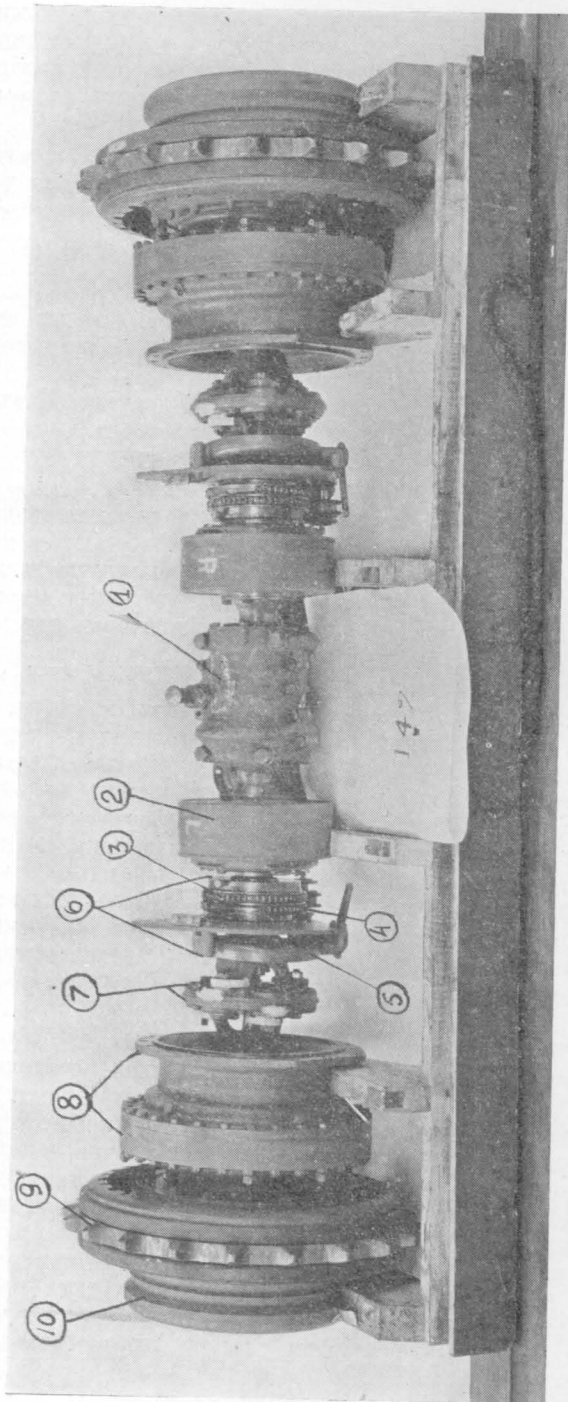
Общий вид трансмиссии (в сборке) от конической передачи до зубчатого ведущего колеса.
